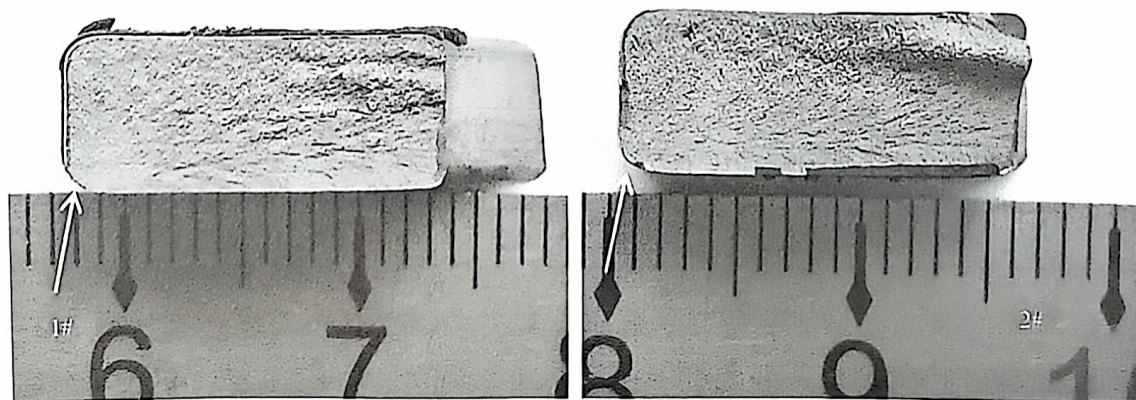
将垫圈裂纹打开后断口的宏观形貌
